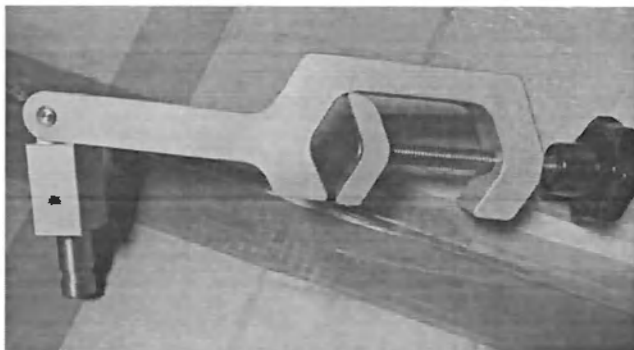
Фотографическое изображение держателя привода резервного насоса
